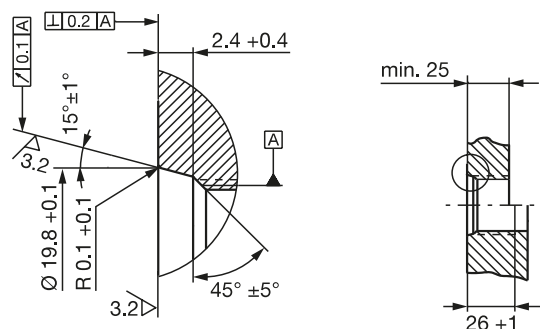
Einschraubloch M18x1.5 nach ISO 6149 O-Ring 15.4x2.1
